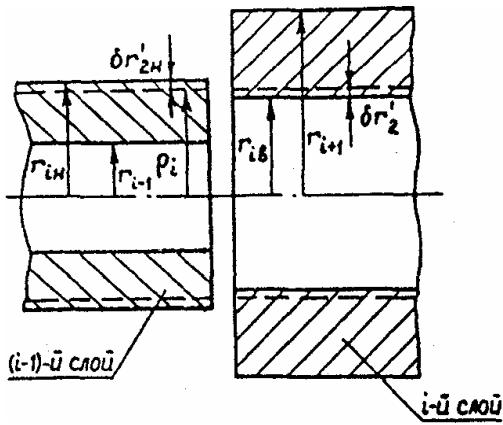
Схема скрепления и размеры слоев скрепленного ствола.
